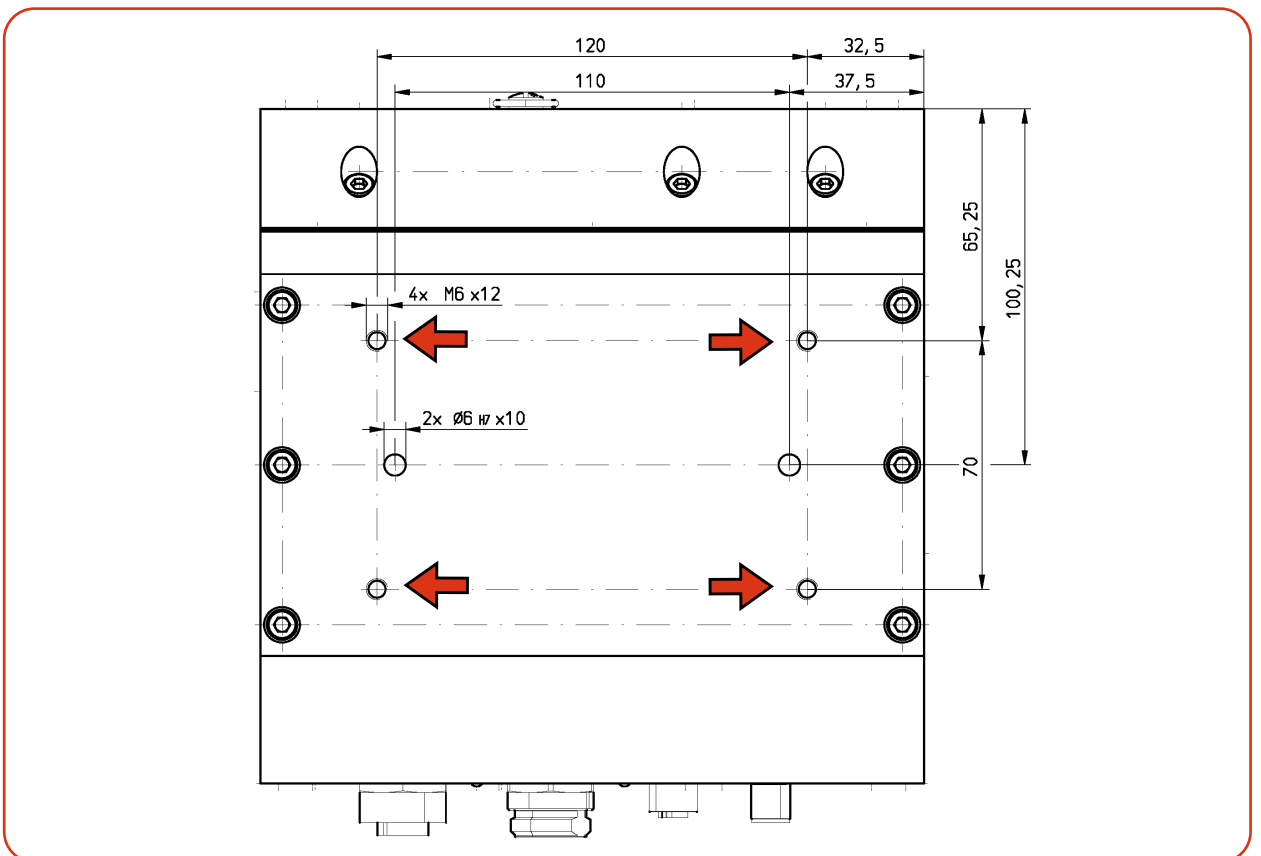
Befestigungsbohrungen im Boden (Ansicht A)
